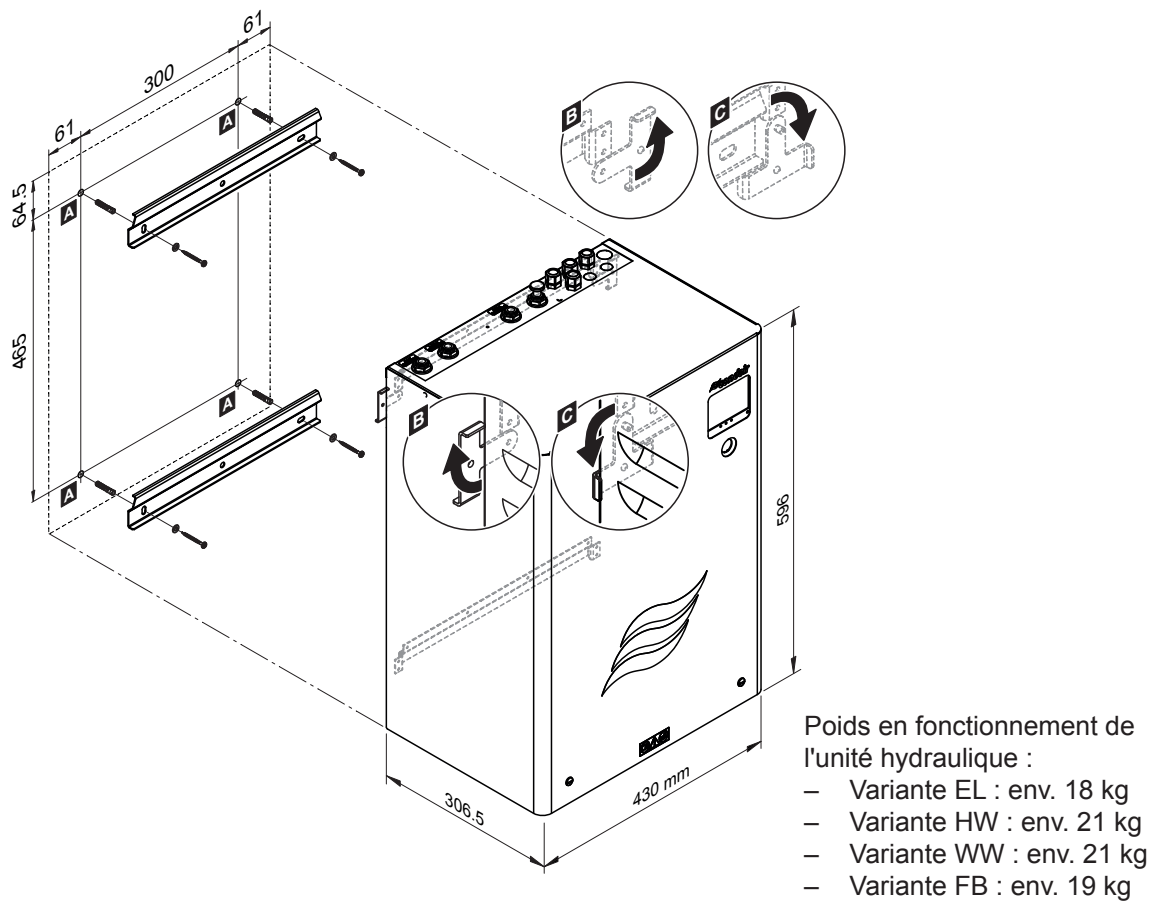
Montage de l'unité hydraulique (dimensions en mm)
